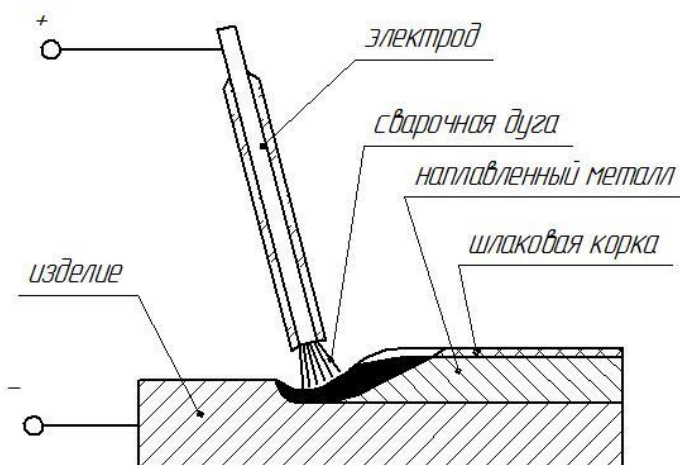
Схема осуществления ручной электродуговой сварки штучными электродами
